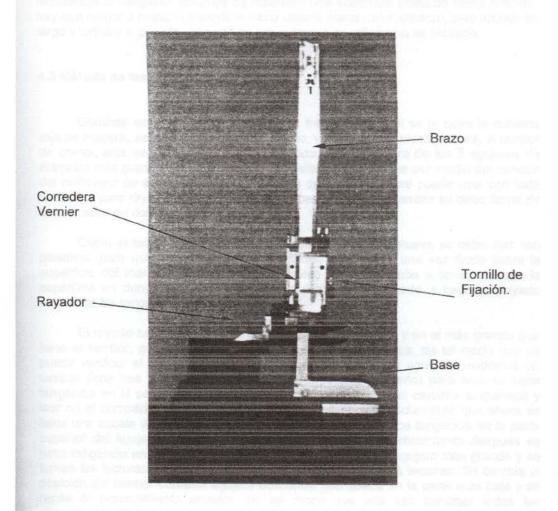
Partes principales de un calibrador de alturas.
